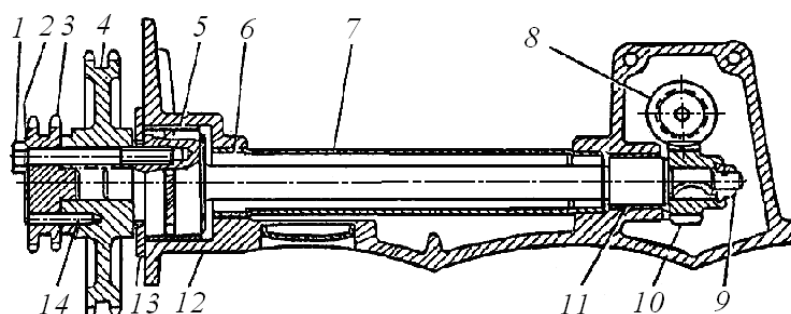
Промежуточный вал: 1 – болт; 2 – стопорная пластина; 3 – ведущая звездочка; 4 – ведомая звездочка; 5 – передняя втулка вала; 6 – промежуточный вал; 7 – труба промежуточного вала; 8 – шестерня ведомая привода масляного насоса; 9 – гайка; 10 – шестерня ведущая привода масляного насоса; 11 – задняя втулка вала; 12 – блок цилиндров; 13 – фланец промежуточного вала; 14 – штифт
